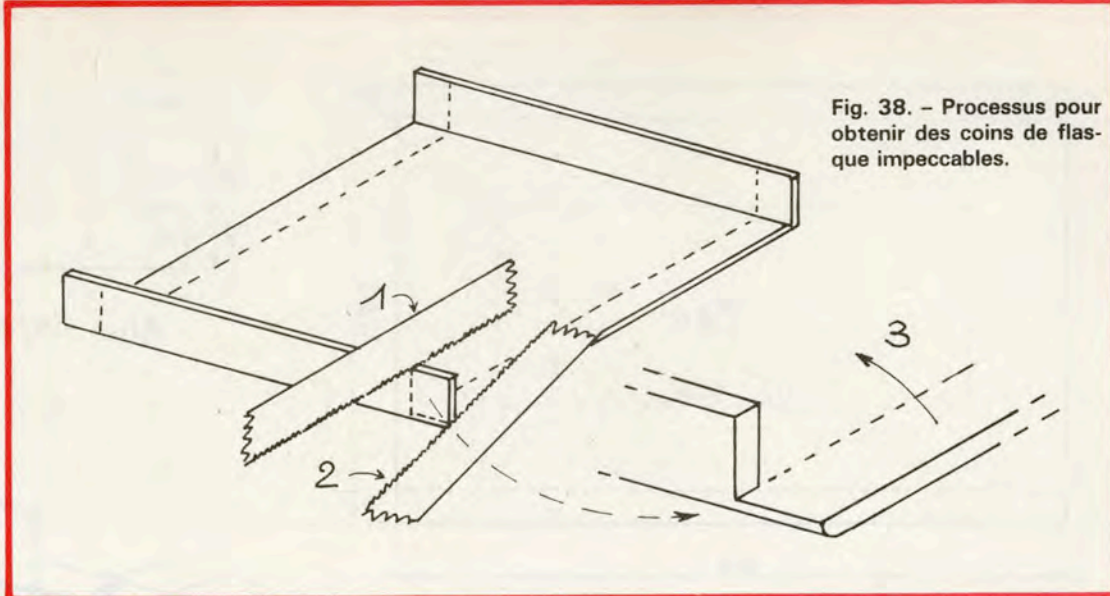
Processus pour obtenir des coins de flasque impeccables.
